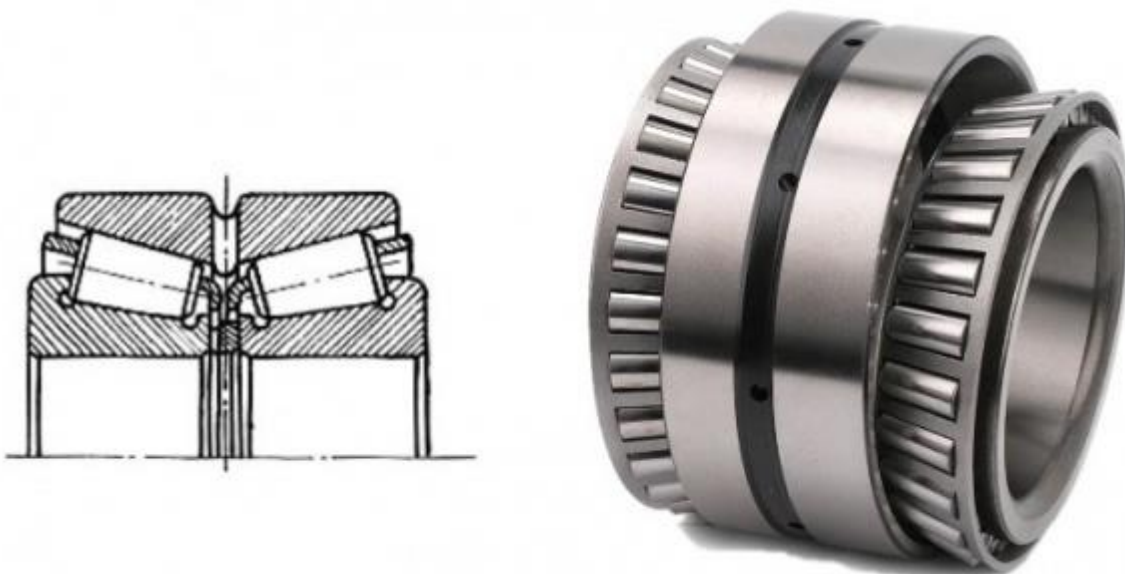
Двухрядный радиально-упорный конический роликовый подшипник
